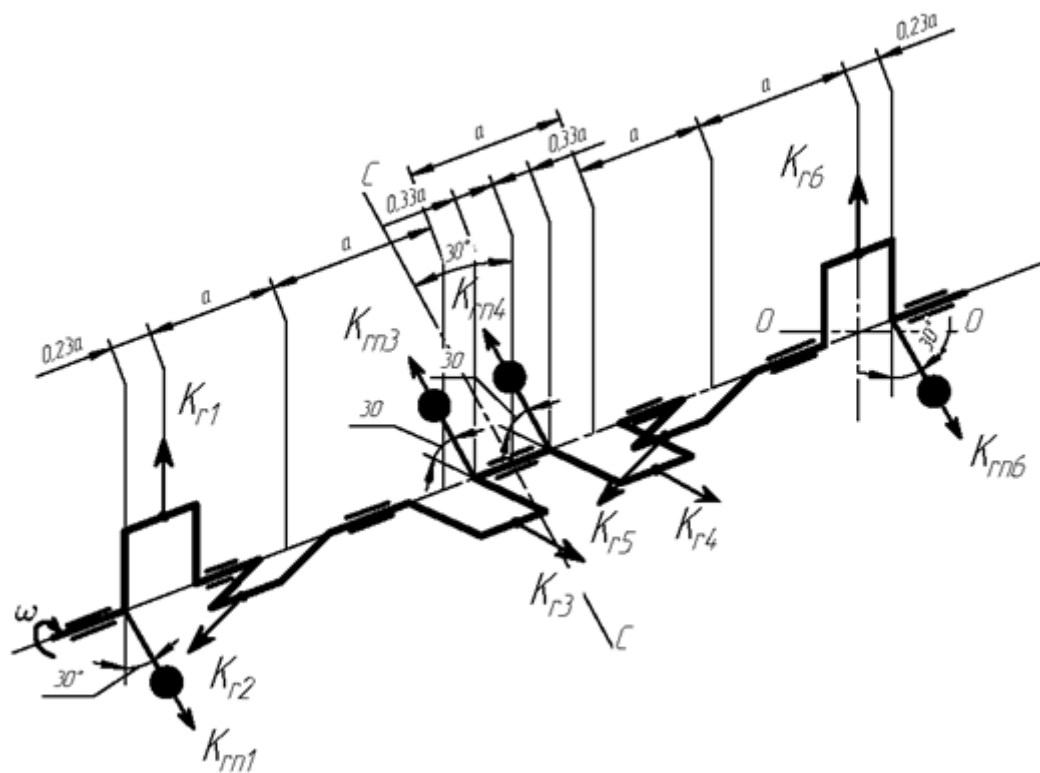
Схема уравнивания коленчатого вала двигателя 6Ч13/14
